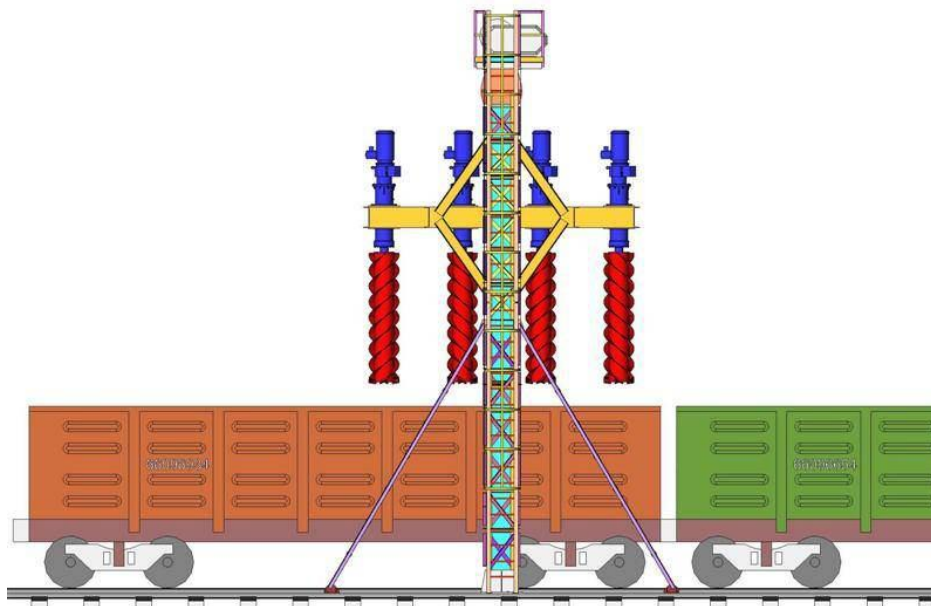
Рыхлитель бурофрезерный РБСМ-4
